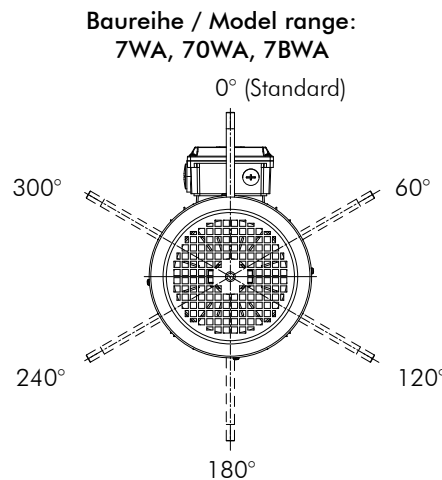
Handlüftung mit Arretierung (Bremse offen)
